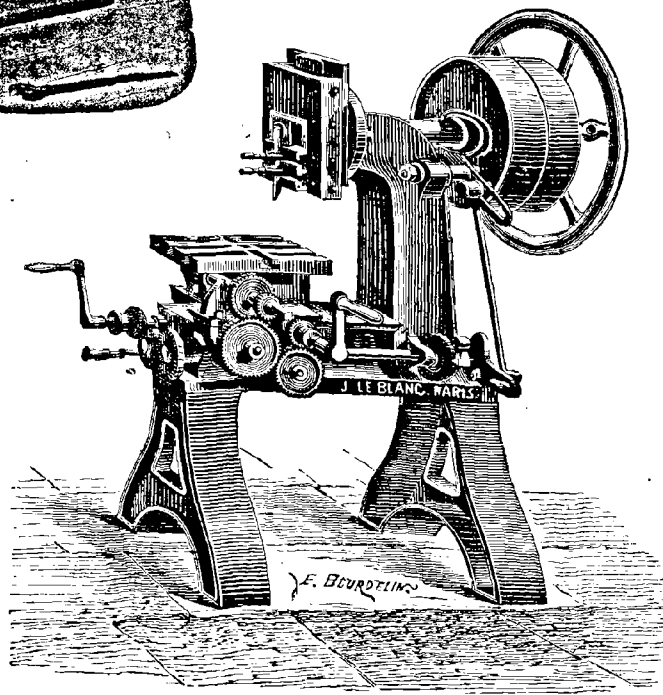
Machine à mortaiser de J. Le Blanc.
